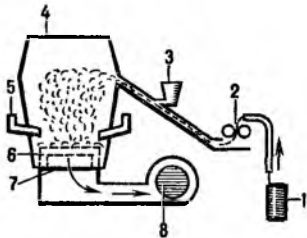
Изготовление заготовок деталей из армированных пластиков методом насасывания 1—бобина со жгутом, 2—резательное устройство, 3—воронка для порошкообразного связующего, 4—камера, 5—пистолет для напыления жидкого связующего, 6—перфорир. форма, 7—вращающийся стол, 8—вентилятор
